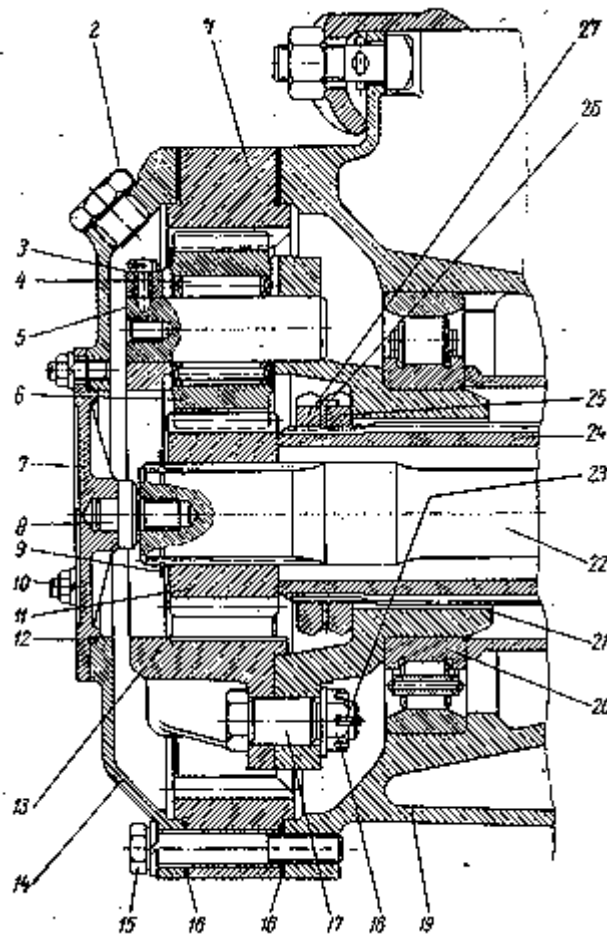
Центральний редуктор тягача МАЗ–МАН 543268:
